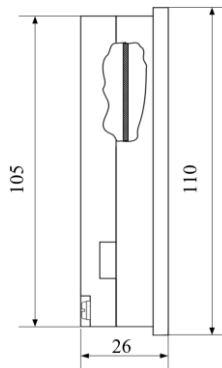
Габаритный чертеж устройства серии МСТ. Вид сбоку
